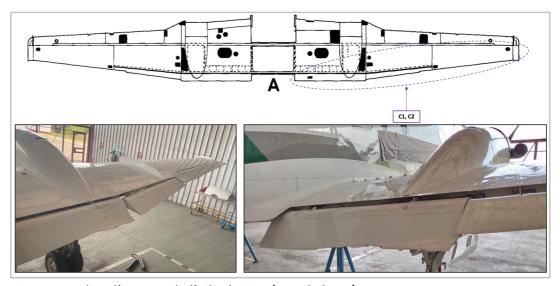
Plan d'impact de l'aile droite (vue de haut)
